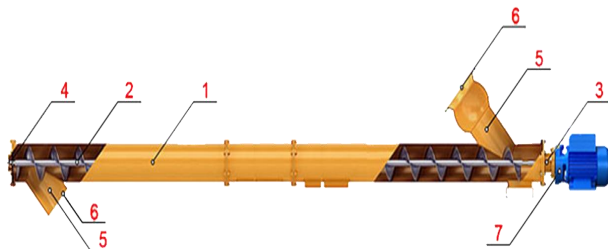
Винтовой горизонтальный конвейер: 1-корпус; 2-винт; 3 - силовой подшипниковый узел; 4 - консольный подшипниковый узел; 5 - загрузочное и разгрузочное отверстие; 6 - присоединительные фланцы; 7 - мотор-редуктор.
